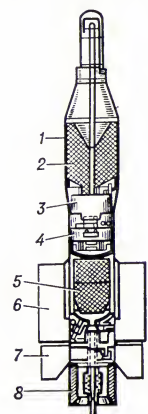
Устройство противотанкового управляемого реактивного снаряда «Виджилент» (Великобритания): 1 — корпус; 2 — кумулятивная боевая часть; 3 — взрыватель; 4 — бортовая аппаратура управления и стабилизации; 5 — реактивный двигатель; 6 — стабилизатор; 7 — руль управления; 8 — катушка с проводом.
